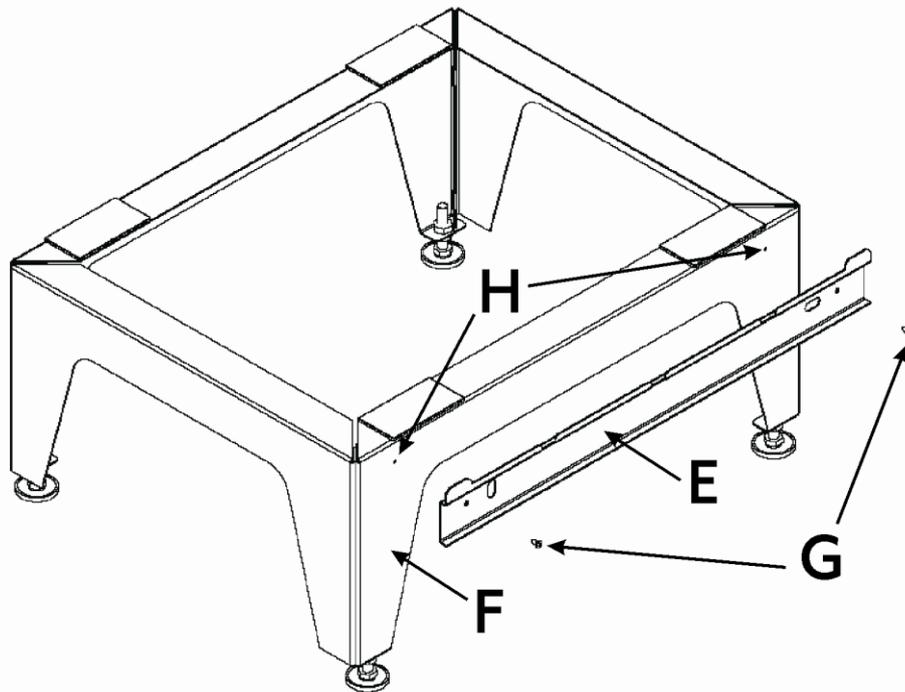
Anschrauben des Befestigungsbleches am Montagerahmen
